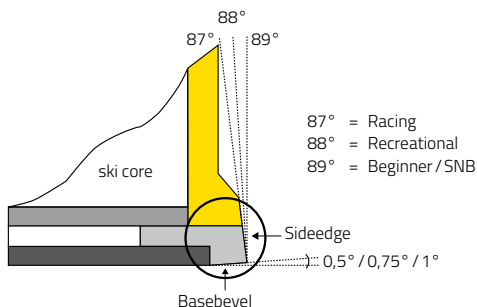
Profesionálové používají pilník, pevný standardní úhel a svorku, kterou pilník k úhelníku připevňují. Nejpoužívanější úhel ve všech disciplínách je 87°. Pro děti a začátečníky jsou nejčastěji používány úhly 88° a 89°.
